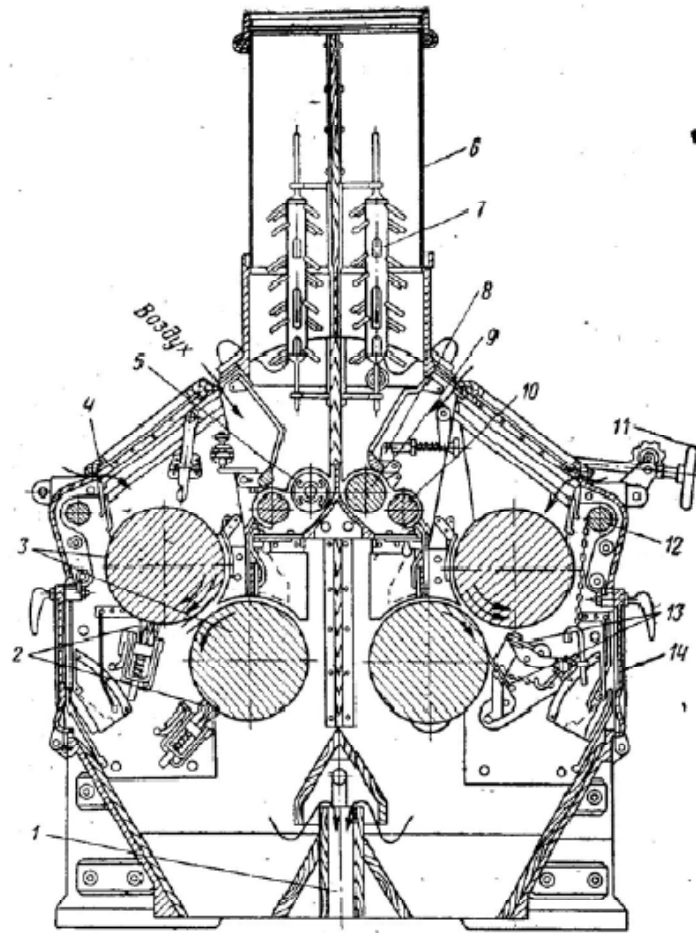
Схема вальцьового верстату типу ЗМ:
